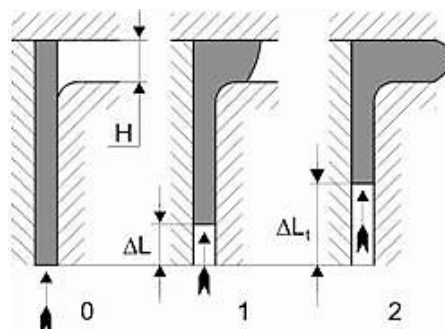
Схема раскатки утолщенных фланцев с выдавливанием: ΔL – подача заготовки на один оборот заготовки; ΔL_1 – суммарная подача; H – толщина фланца; стадии раскатки: 0 – начальная, 1 – промежуточная, 2 – окончательная
